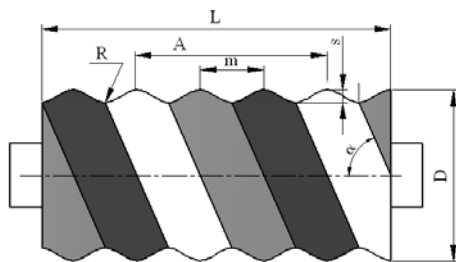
Основные геометрические параметры геликоидального валка: D – диаметр валка по выступам; A – шаг захода; m – шаг между выступами; s – высота выступа; R– радиус закругления выступа и впадины ; L – длина бочки валка.
